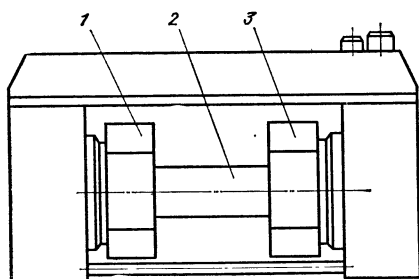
Компоновка приспособления с двумя барабанами, сидящими на общей оси
